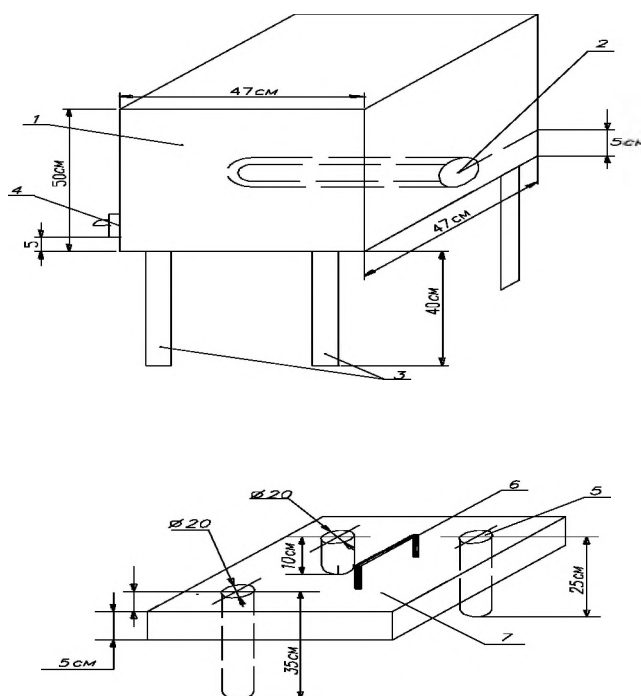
Схема экспериментального стенда бака-аккумулятора 1-корпус; 2- электронагреватель, 3- опорные ножки, 4- сливной вентиль, 5- гнезда для термометра, 6-крышка корпуса.
